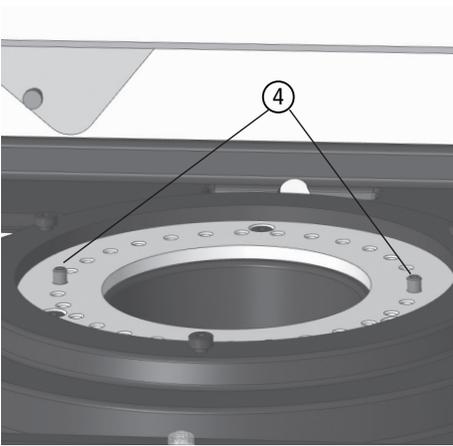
Tiges de butée, réglage des butées gauche et droite
